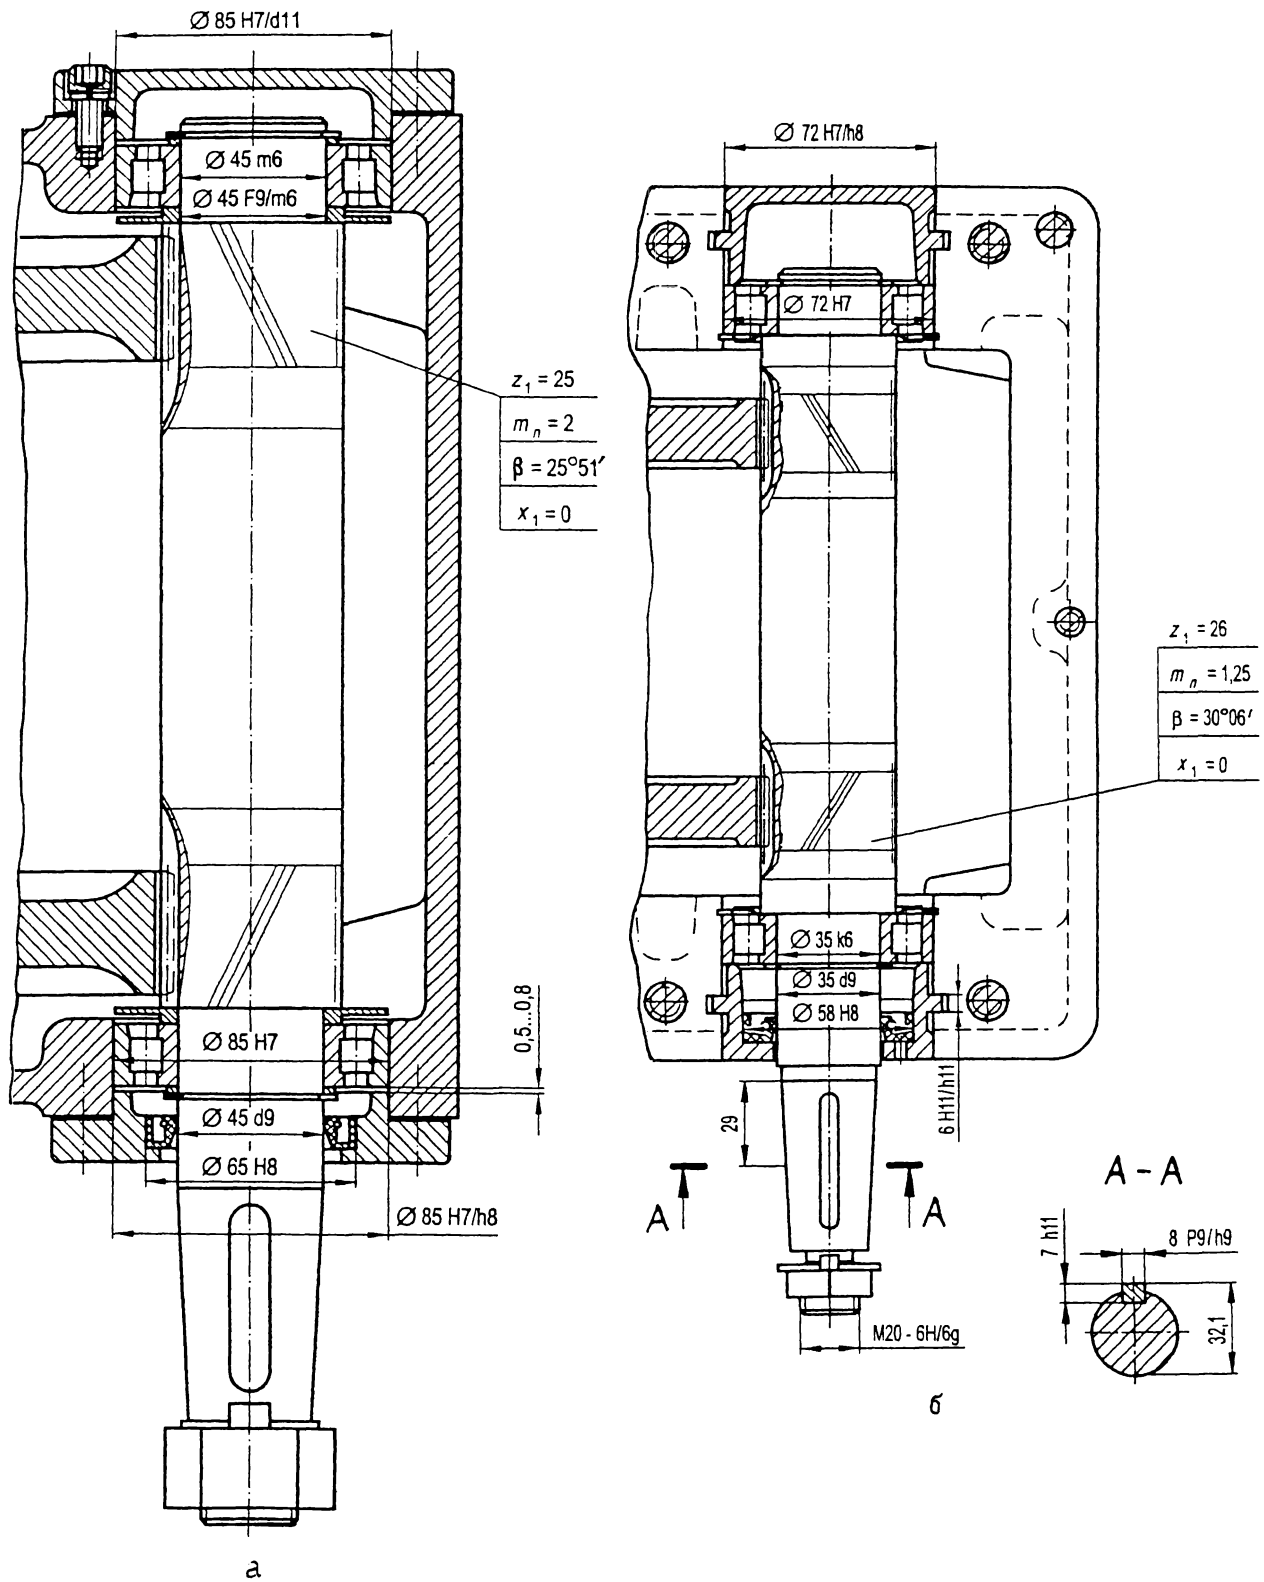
Примеры конструкций быстроходных (входных) плавающих валов раздвоенных (шевронных) зубчатых передач [1, 3]
